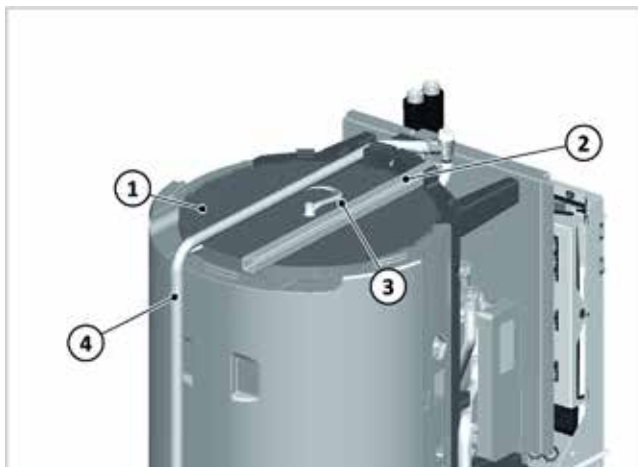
installation du rond de couvercle et des goulottes de câble
